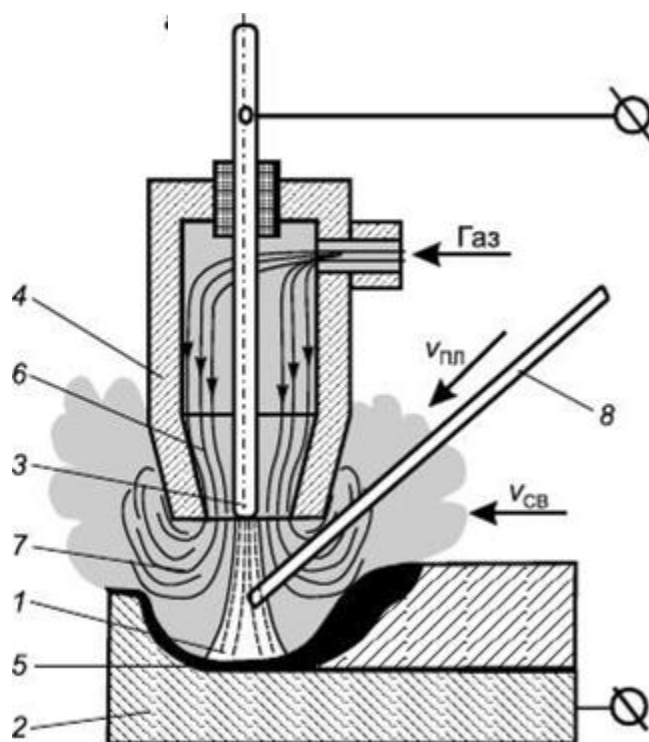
Схема процесса дуговой сварки в защитных газах неплавящимся электродом: 1 – дуга; 2 – изделие; 3 – электрод; 4 – сопло; 5 – сварочная ванна; 6 – поток газа; 7 – защитное облако; 8 – присадочный пруток
